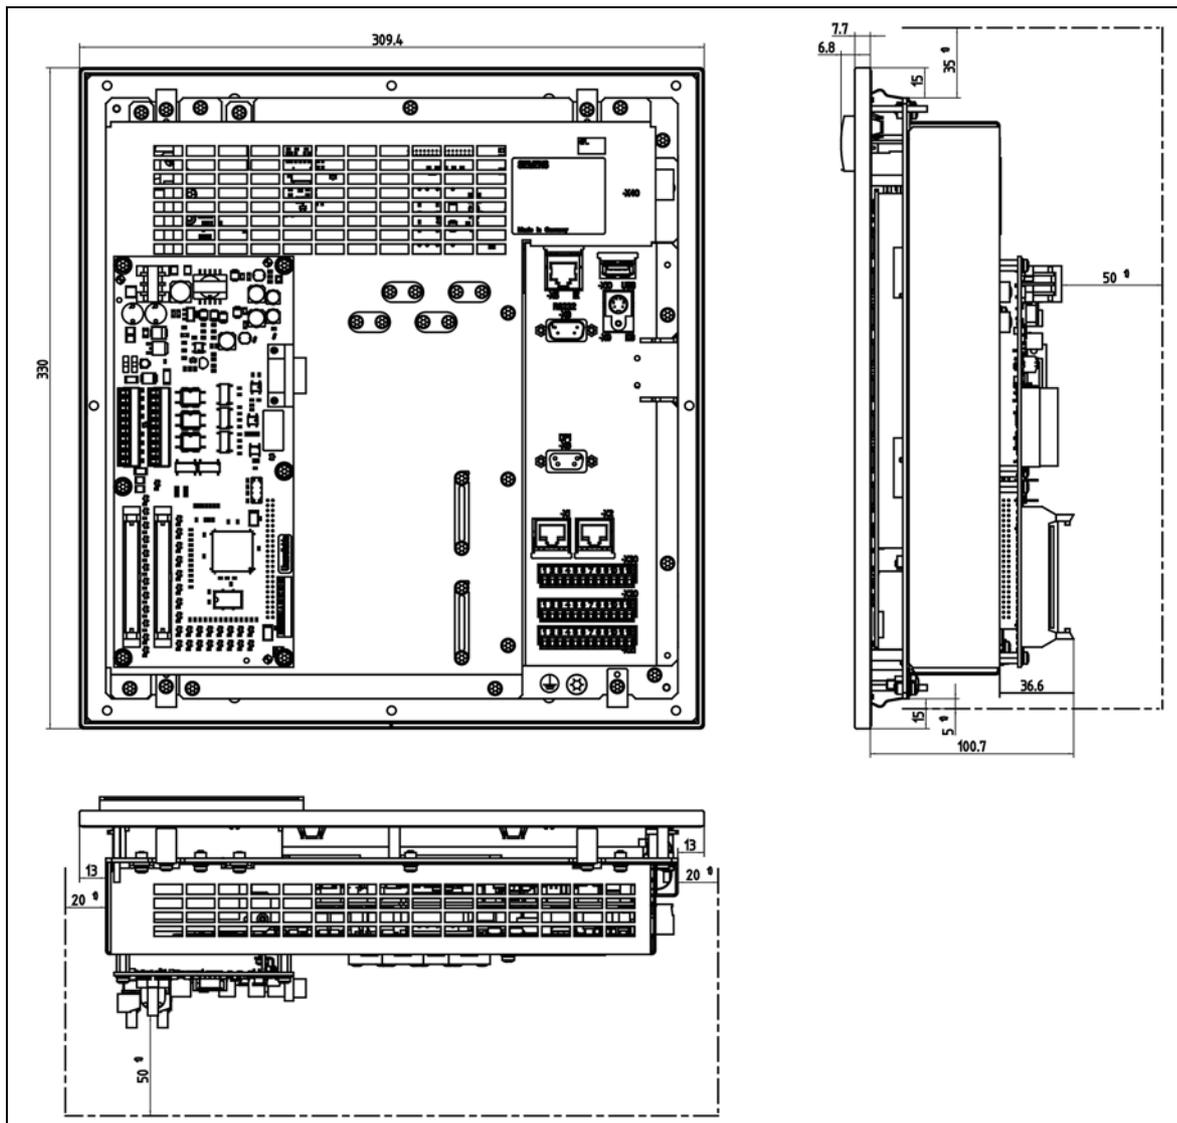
带 MCPA 模块的 CNC 操作面板的外形尺寸图
